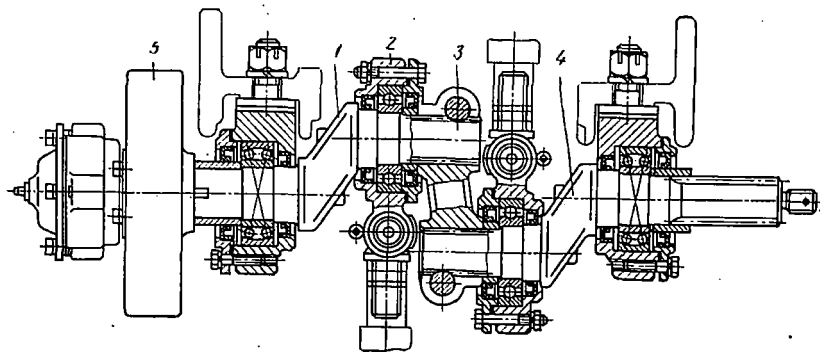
Коленчатый вал привода аппаратов косилки КНУ-6
